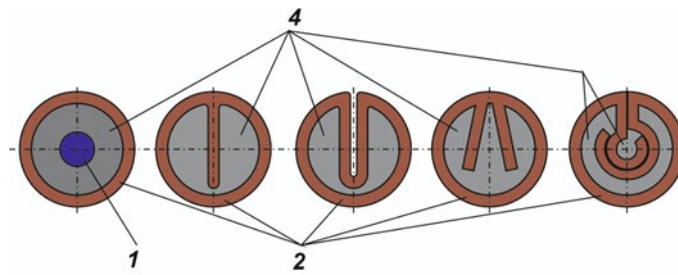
Різні типи порошкових дротів, що використовуються для електрошлакового наплавлення: 1 – металеві стрижні; 2 – металева оболонка; 3 - опресоване покриття; 4 – порошкоподібна шихта
